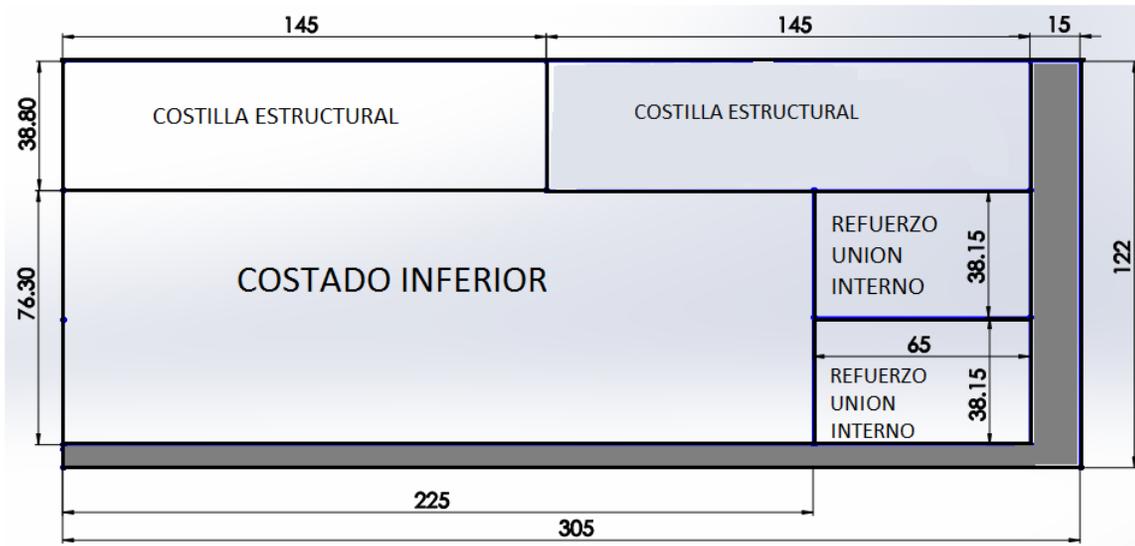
Reestructuración y rediseño de plantilla de corte (fuente: elaboración propia)
